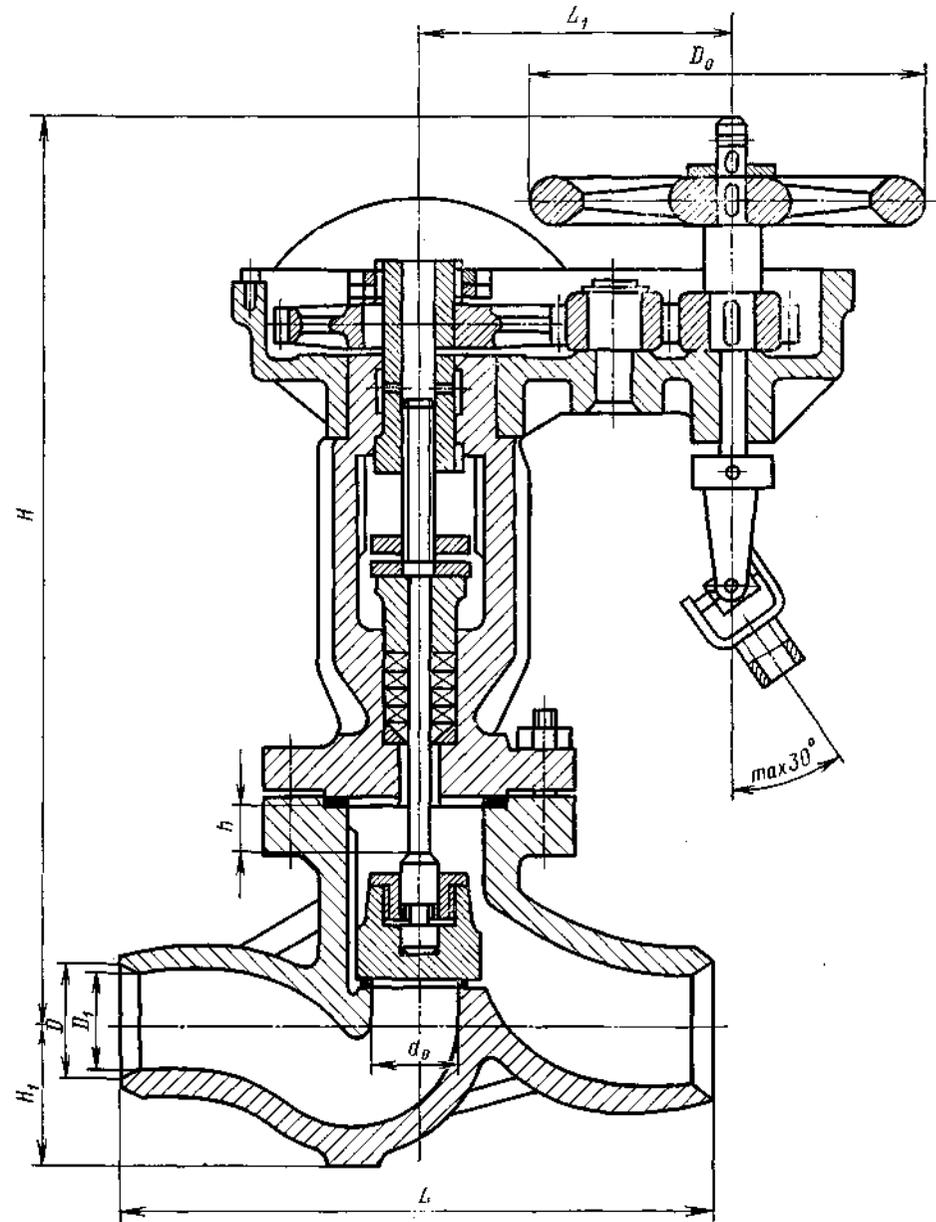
Вентили Т-1106 и Т-1136 с приводной головкой и цилиндрической передачей D , 100, 150
